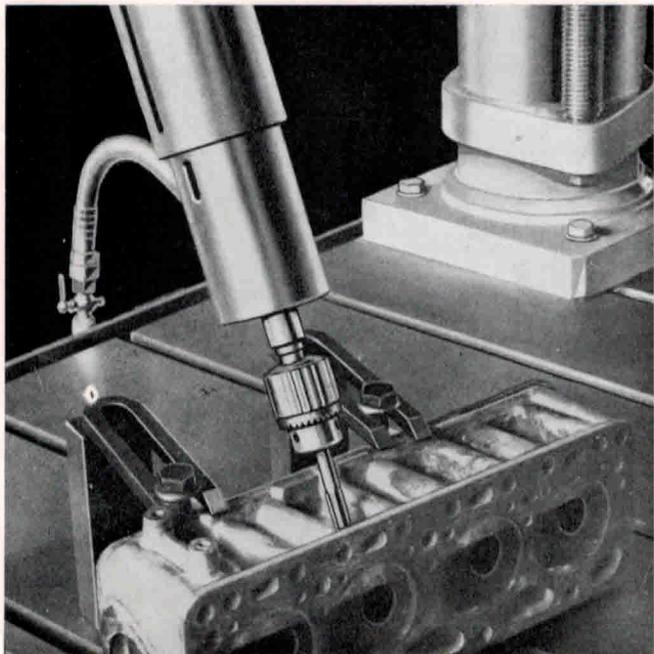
Bohrmaschine mit Ausdrehwerkzeug
